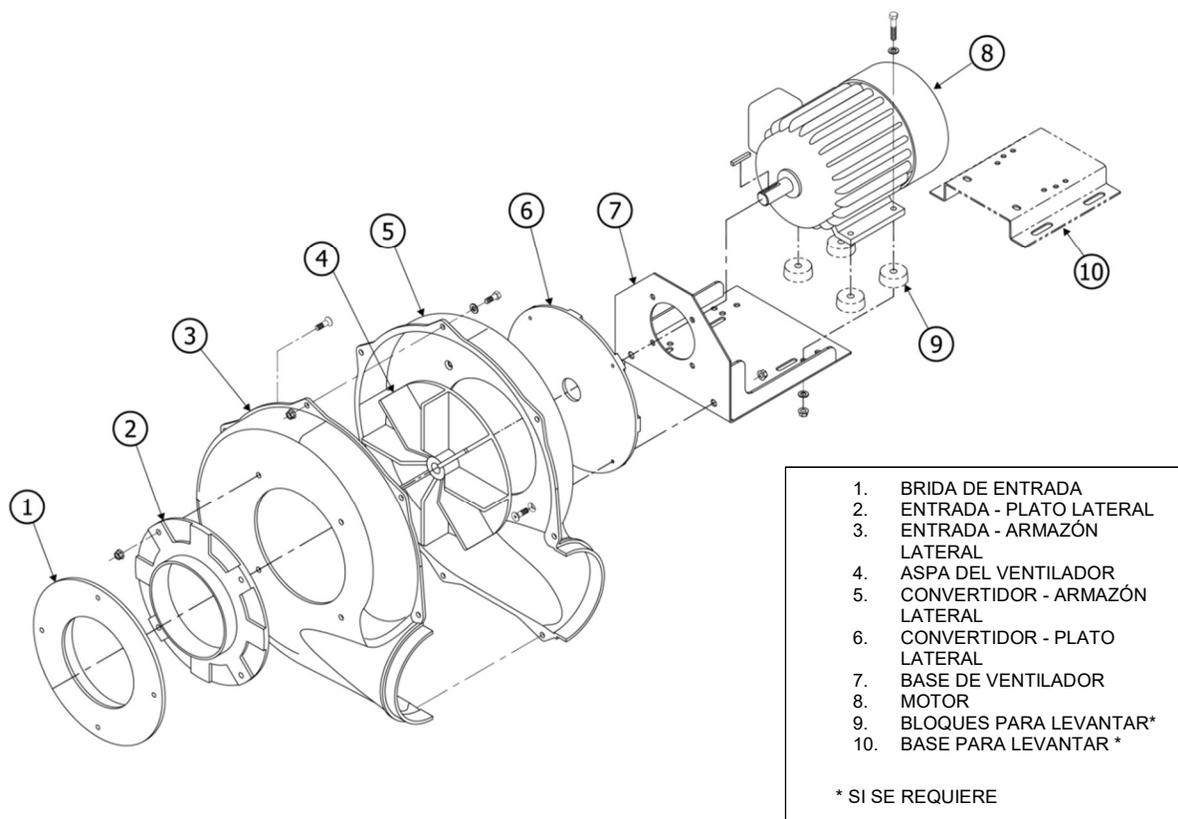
Vista detallada del Ventilador de Benchmark 6000
